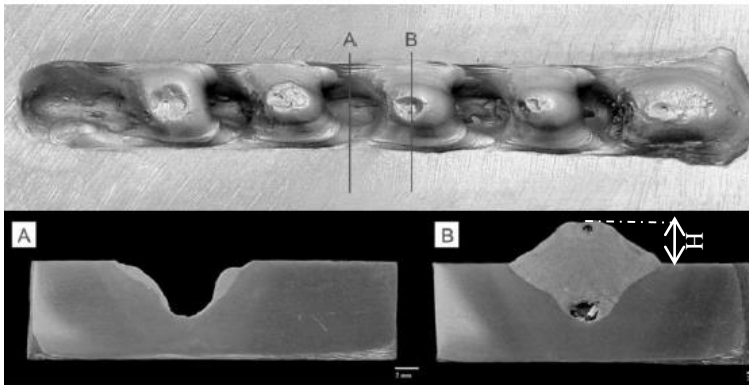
Exemplo de *humping* em soldagem TIG [1]
